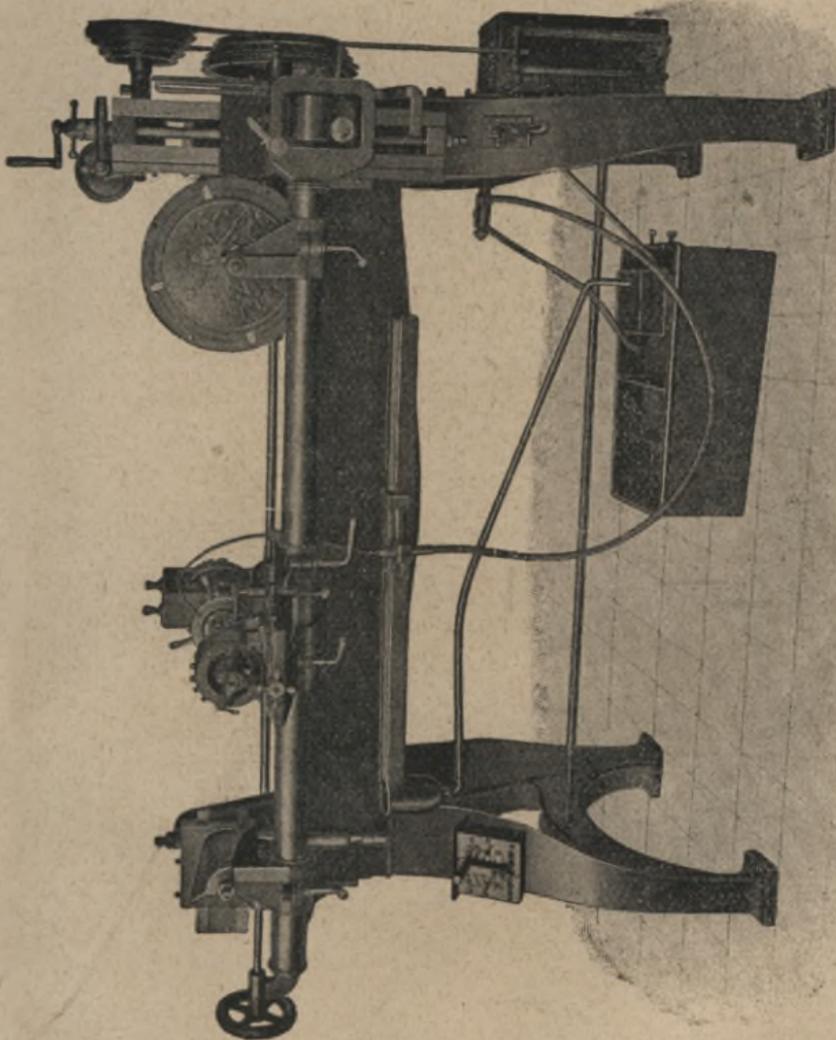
Reliefkopiermaschine der Leipziger Maschinenbau-Gesellschaft.
